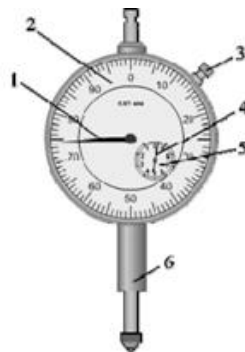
Індикатор годинникового типу: 1 – велика стрілка; 2 – шкала індикатора; 3 – стопор; 4 – стрілка; 5 – відлікова шкала; 6 – вимірювальний стрижень.
